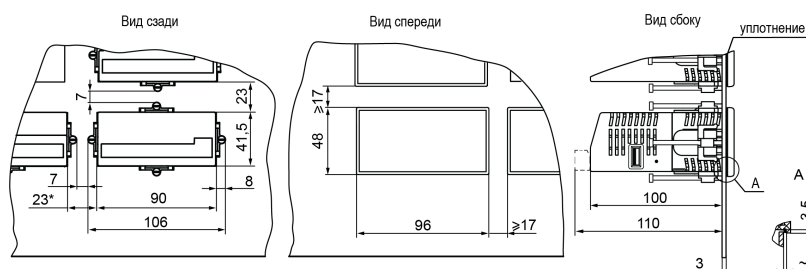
Прибор в корпусе Щ2, установленный в щит толщиной 3 мм
